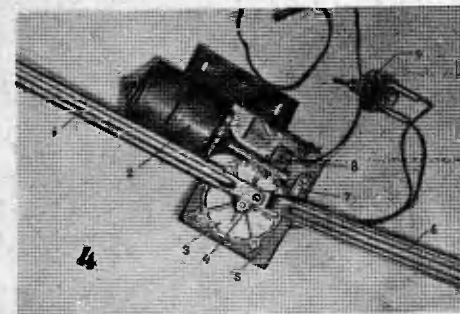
Механизм в сборе: 1 — правая тяга; 2 — электродвигатель; 3 — редуктор; 4 — кривошип; 5 — кронштейн; 6 — левая тяга; 7 — сопротивление и концевой выключатель; 8 — биметаллический предохранитель; 9 — выключатель (ВТЗ.602.014).
